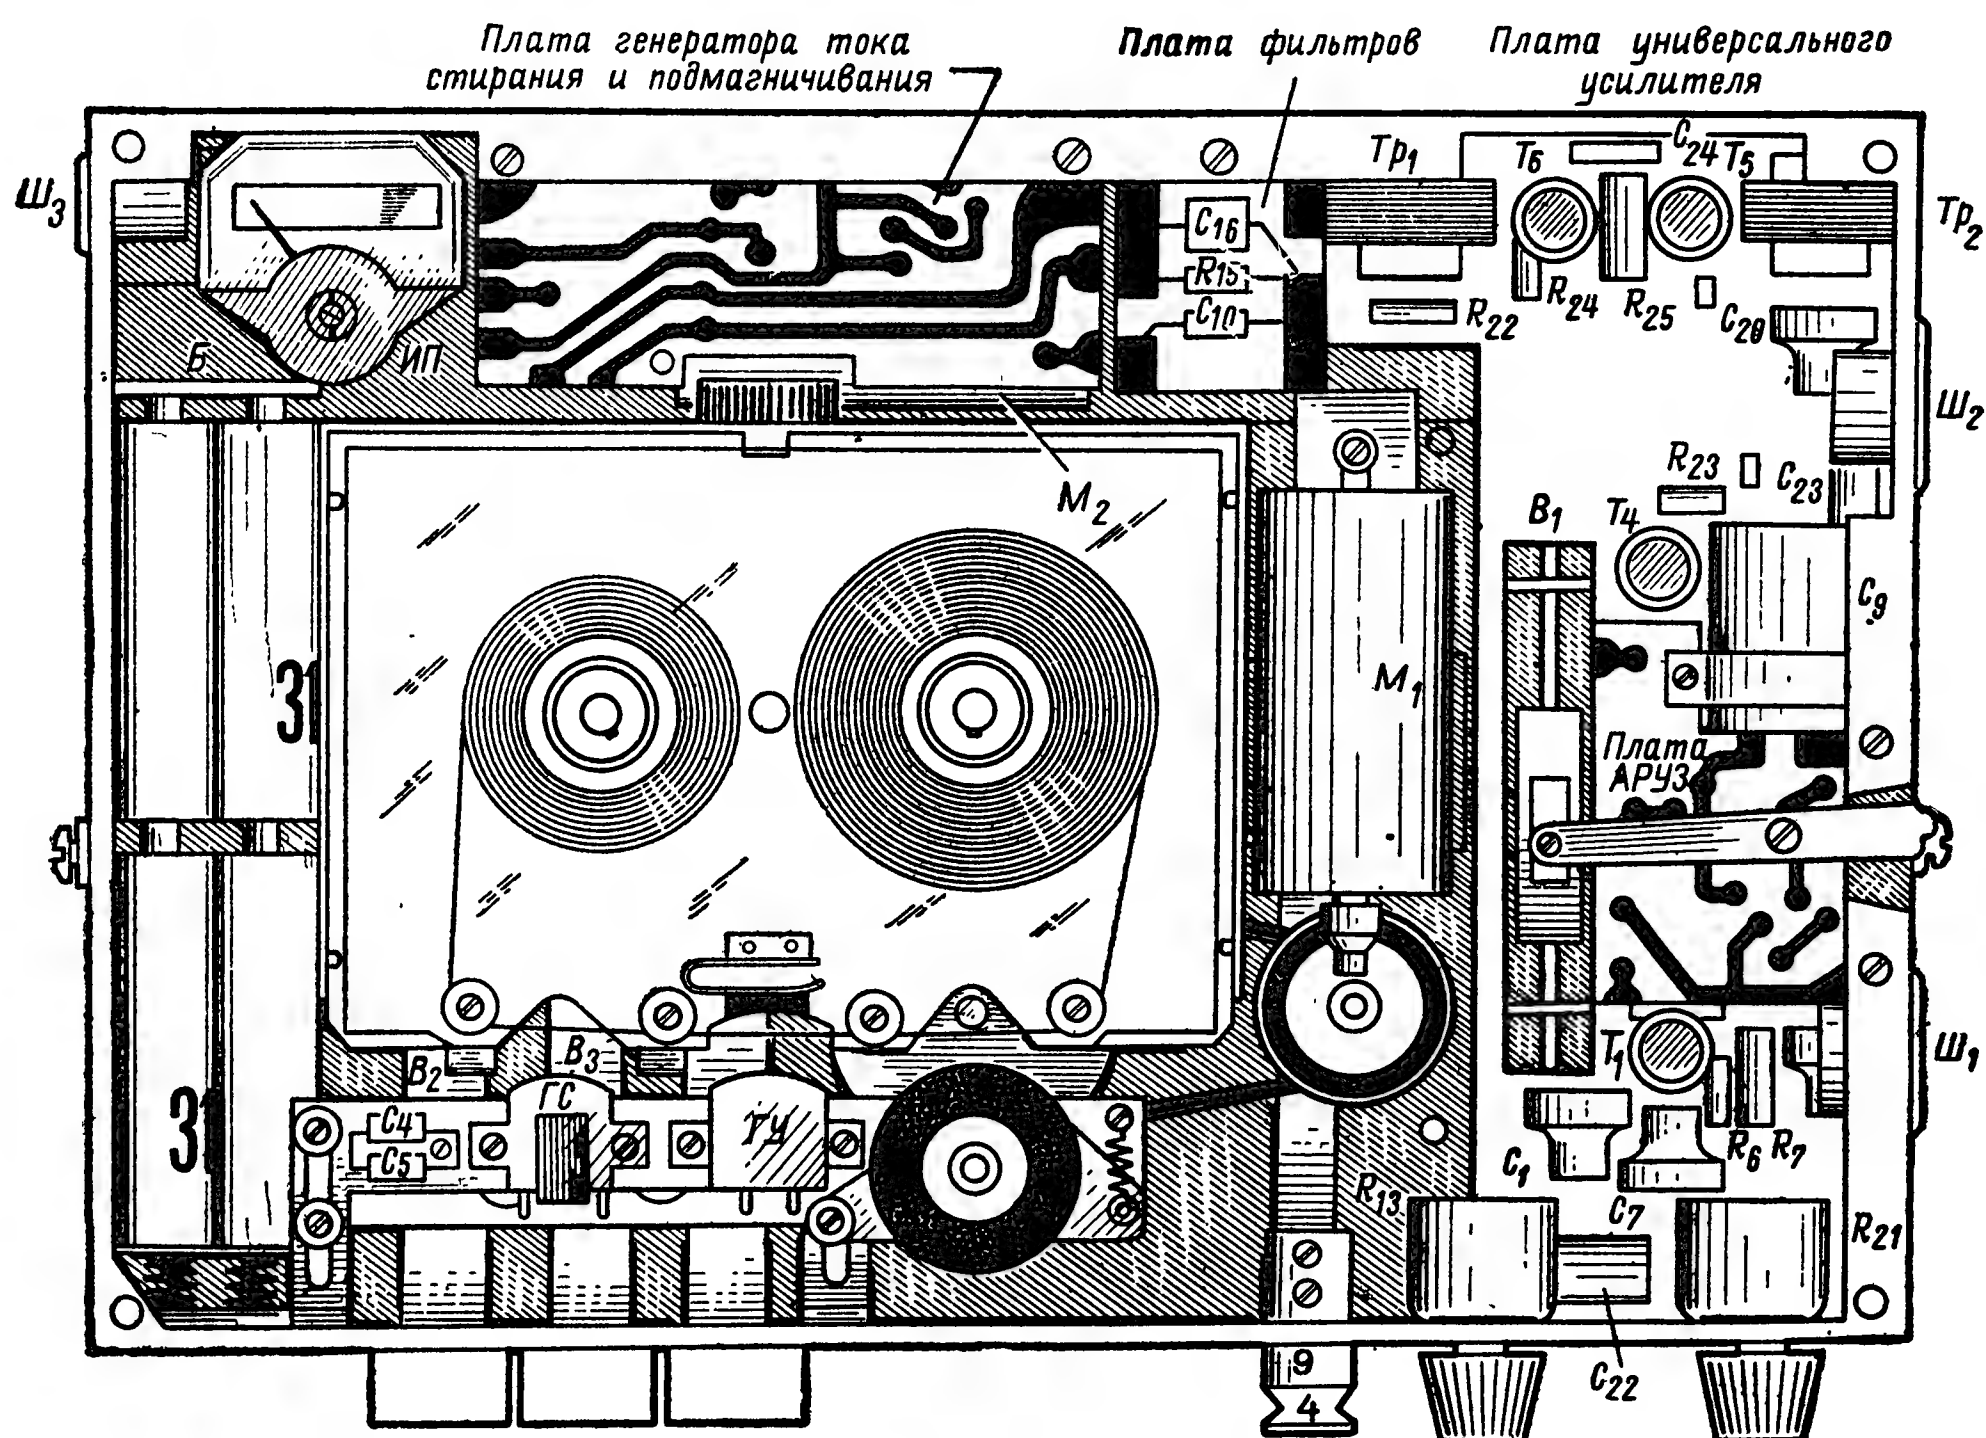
Расположение деталей в корпусе магнитофона (верхняя панель снята).
